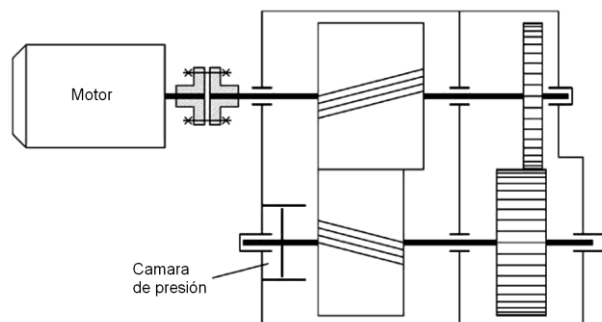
Máquina para ensayo de engranajes Ryder [71].
